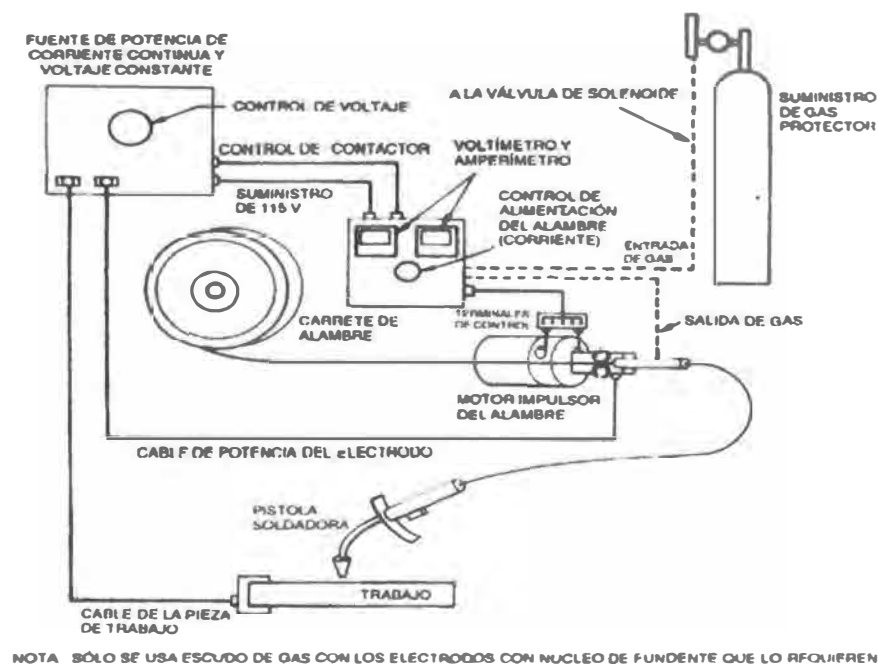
Equipo de soldeo con alambre tubular (FCAW)
